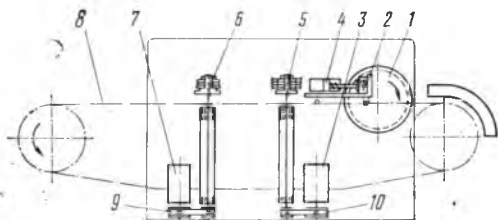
Кинематическая схема одностороннего шипорезного полуавтомата для нарезания зубчатых шипов
